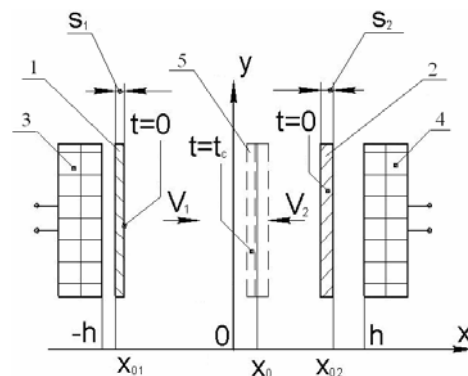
Схема зустрічного зштовхування заготовок при магнітно-імпульсному зварюванні: 1, 2 – початкове положення зварюваних заготовок; 3, 4 – нерухомі індуктори; 5 – положення зварюваних заготовок в момент удару t_c .
